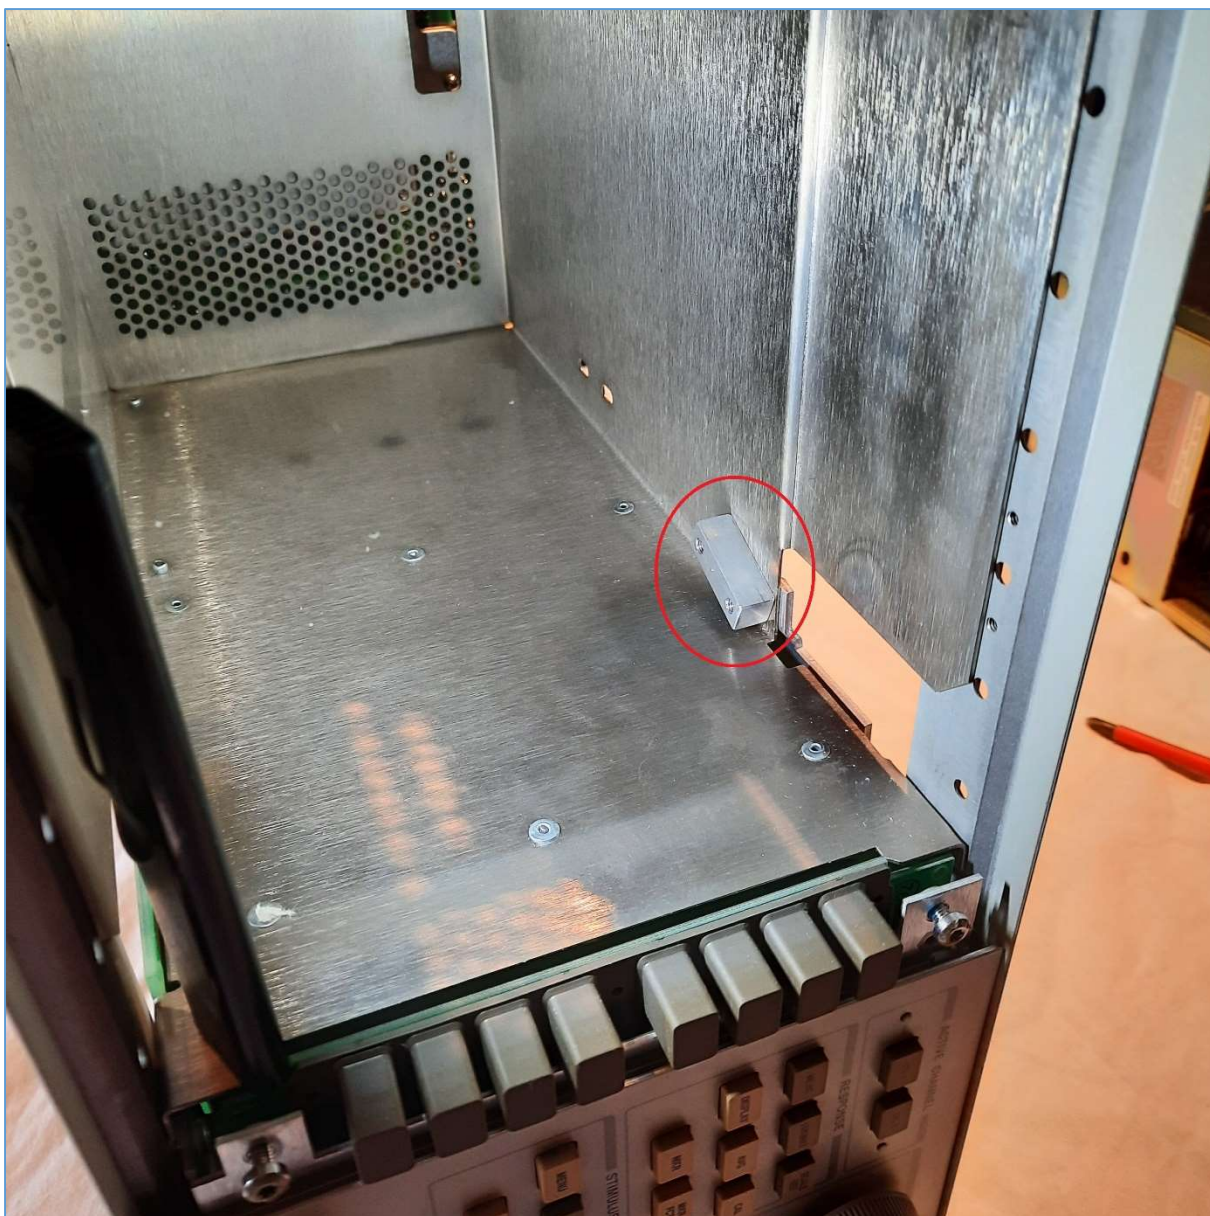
Barreau de fixation de la patte d'arrimage du bloc YTO du VNA ; vue par l'intérieur de la cavité du rack. Photo : ON4IJ.
